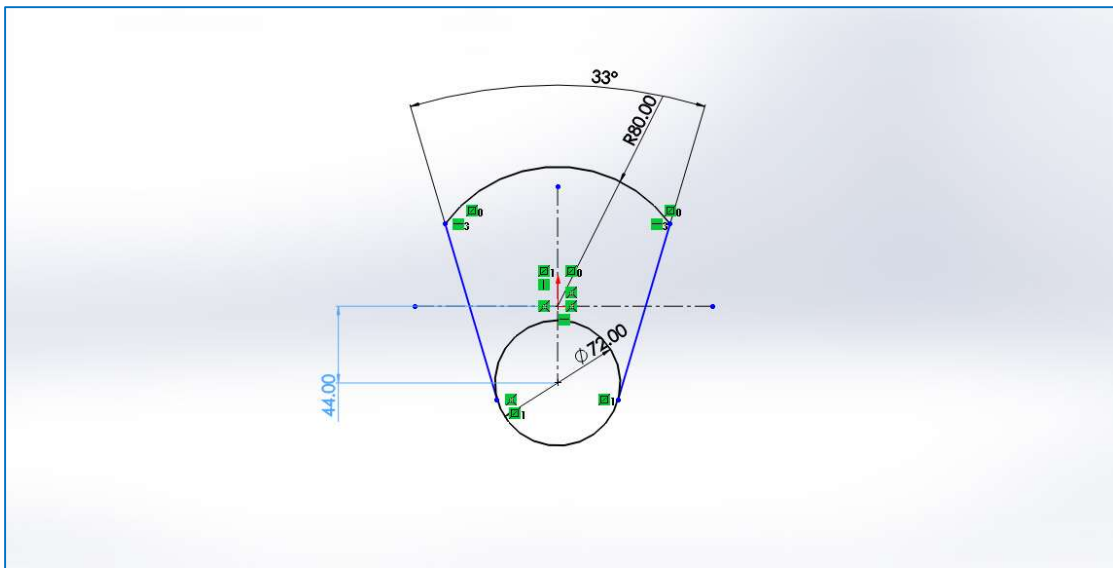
Étape de la construction d'une forme 2D de vilebrequin
